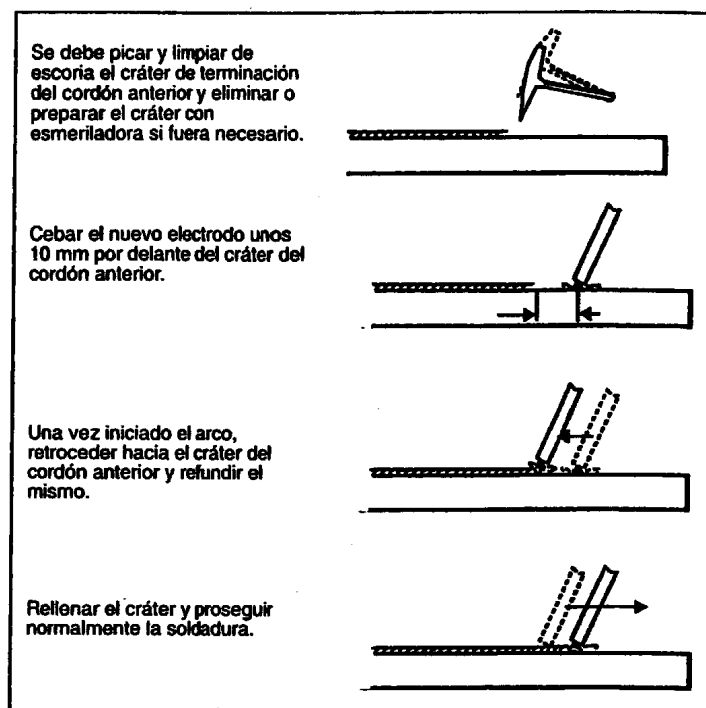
REALIZACIÓN CORRECTA DE LOS EMPALMES DE LOS CORDONES DE SOLDADURA
